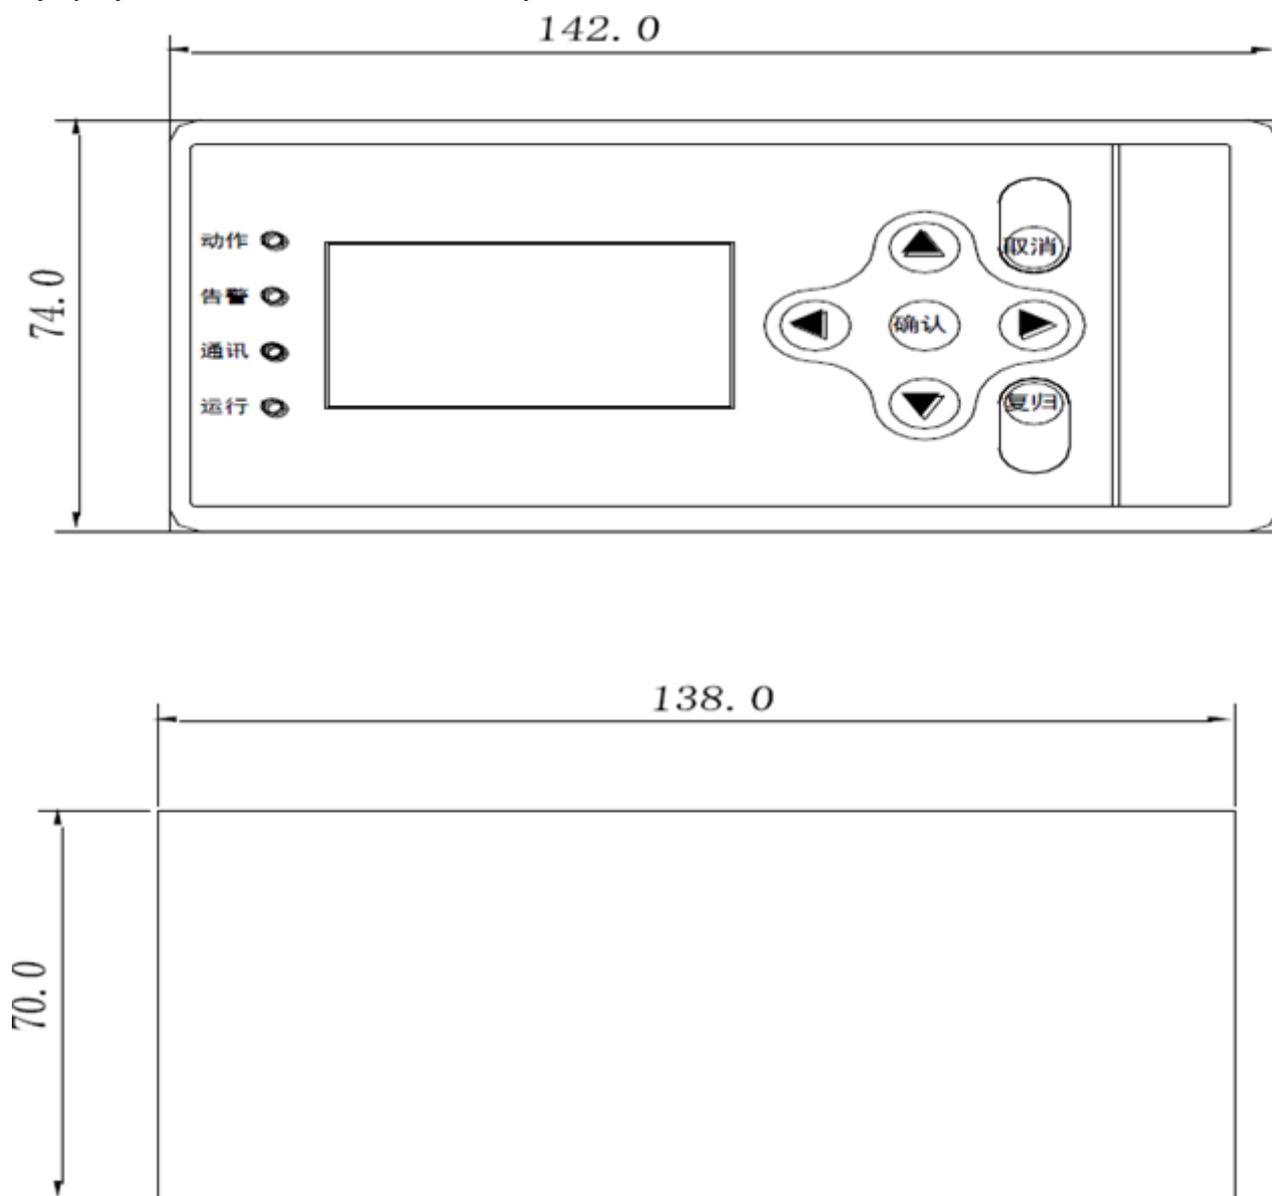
Чертеж панели и отверстия для установки устройства. Размеры отверстия для устройства
